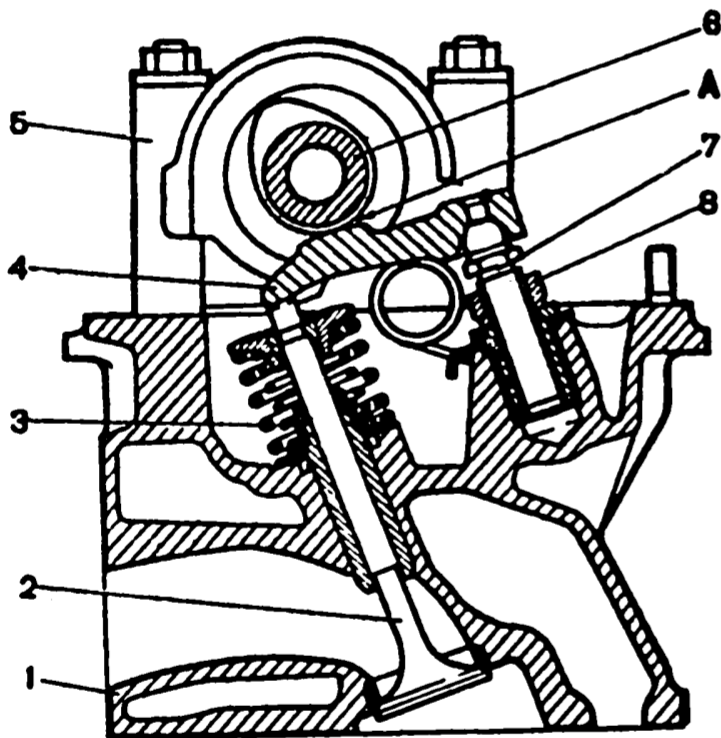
Разрез головки цилиндров по выпускному клапану: 1 - головка цилиндров; 2 - выпускной клапан; 3 - маслоотражательный колпачок; 4 - рычаг клапана; 5 - корпус подшипников распределительного вала; 6 - распределительный вал; 7 - регулировочный болт; 8 - контргайка болта; А - зазор между рычагом и кулачком распределительного вала
